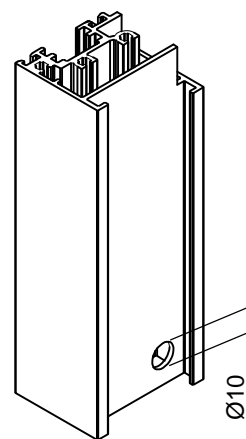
x 45. Povezivanje vertikalnog pojasa rama F-1600 i praga F-1612
